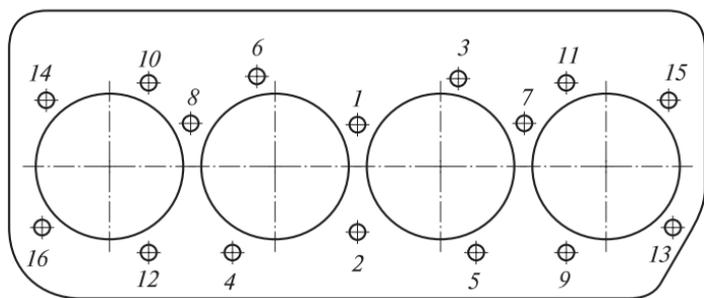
Последовательность (1—16) затяжки болтов крепления головки цилиндров
